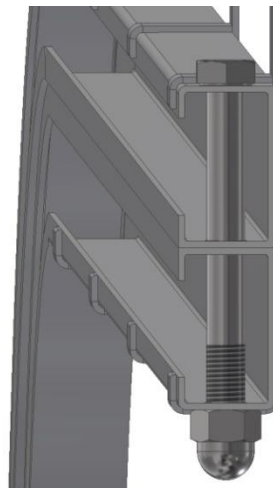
Upevnění kolečka k rámu [autor]
